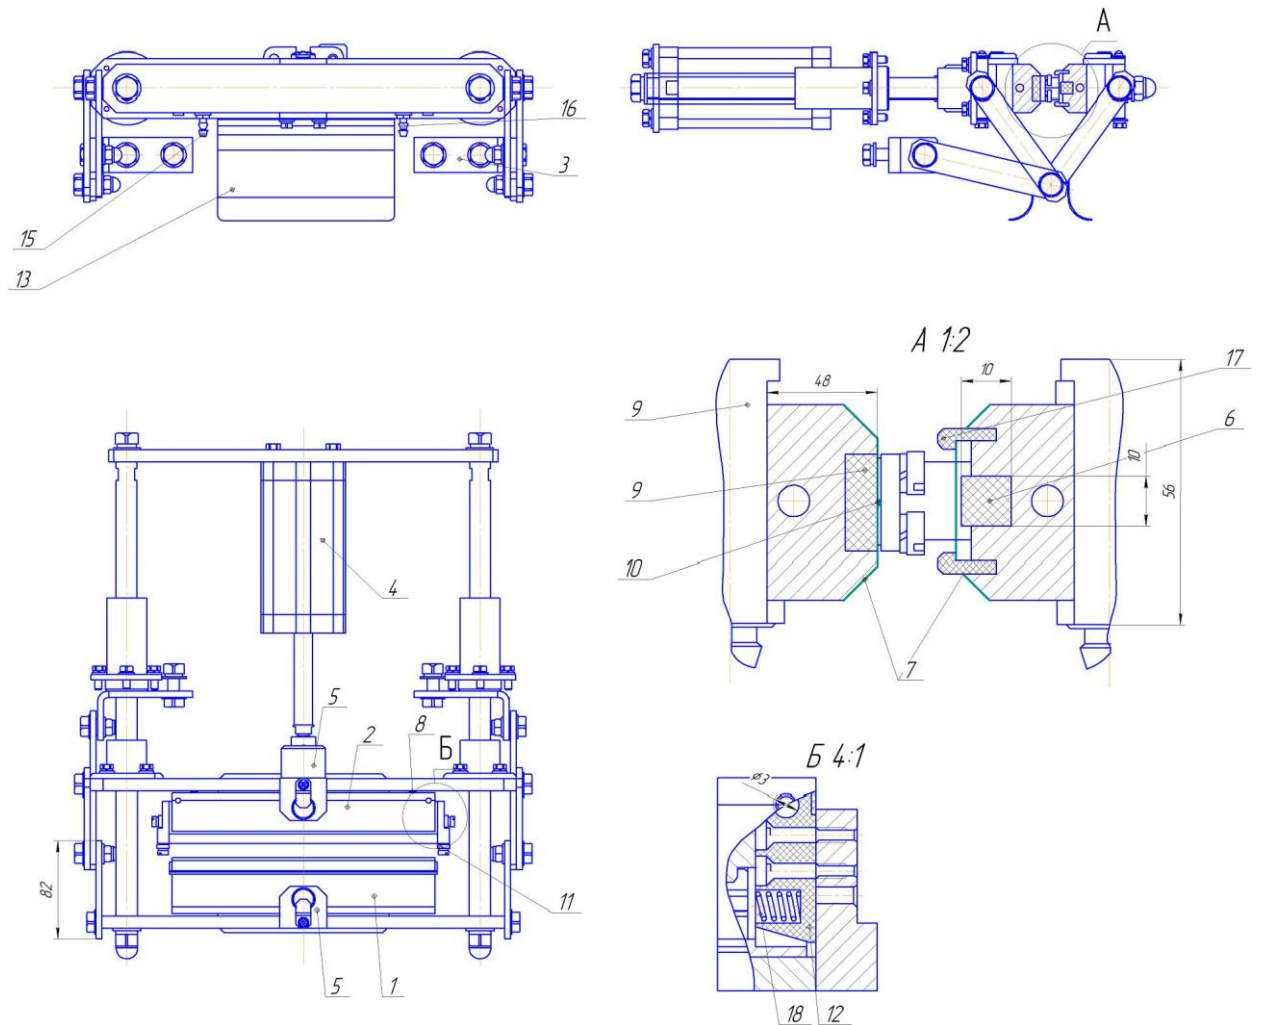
Механізм поперечної зварки: 1 – корпус; 2 – корпус;
